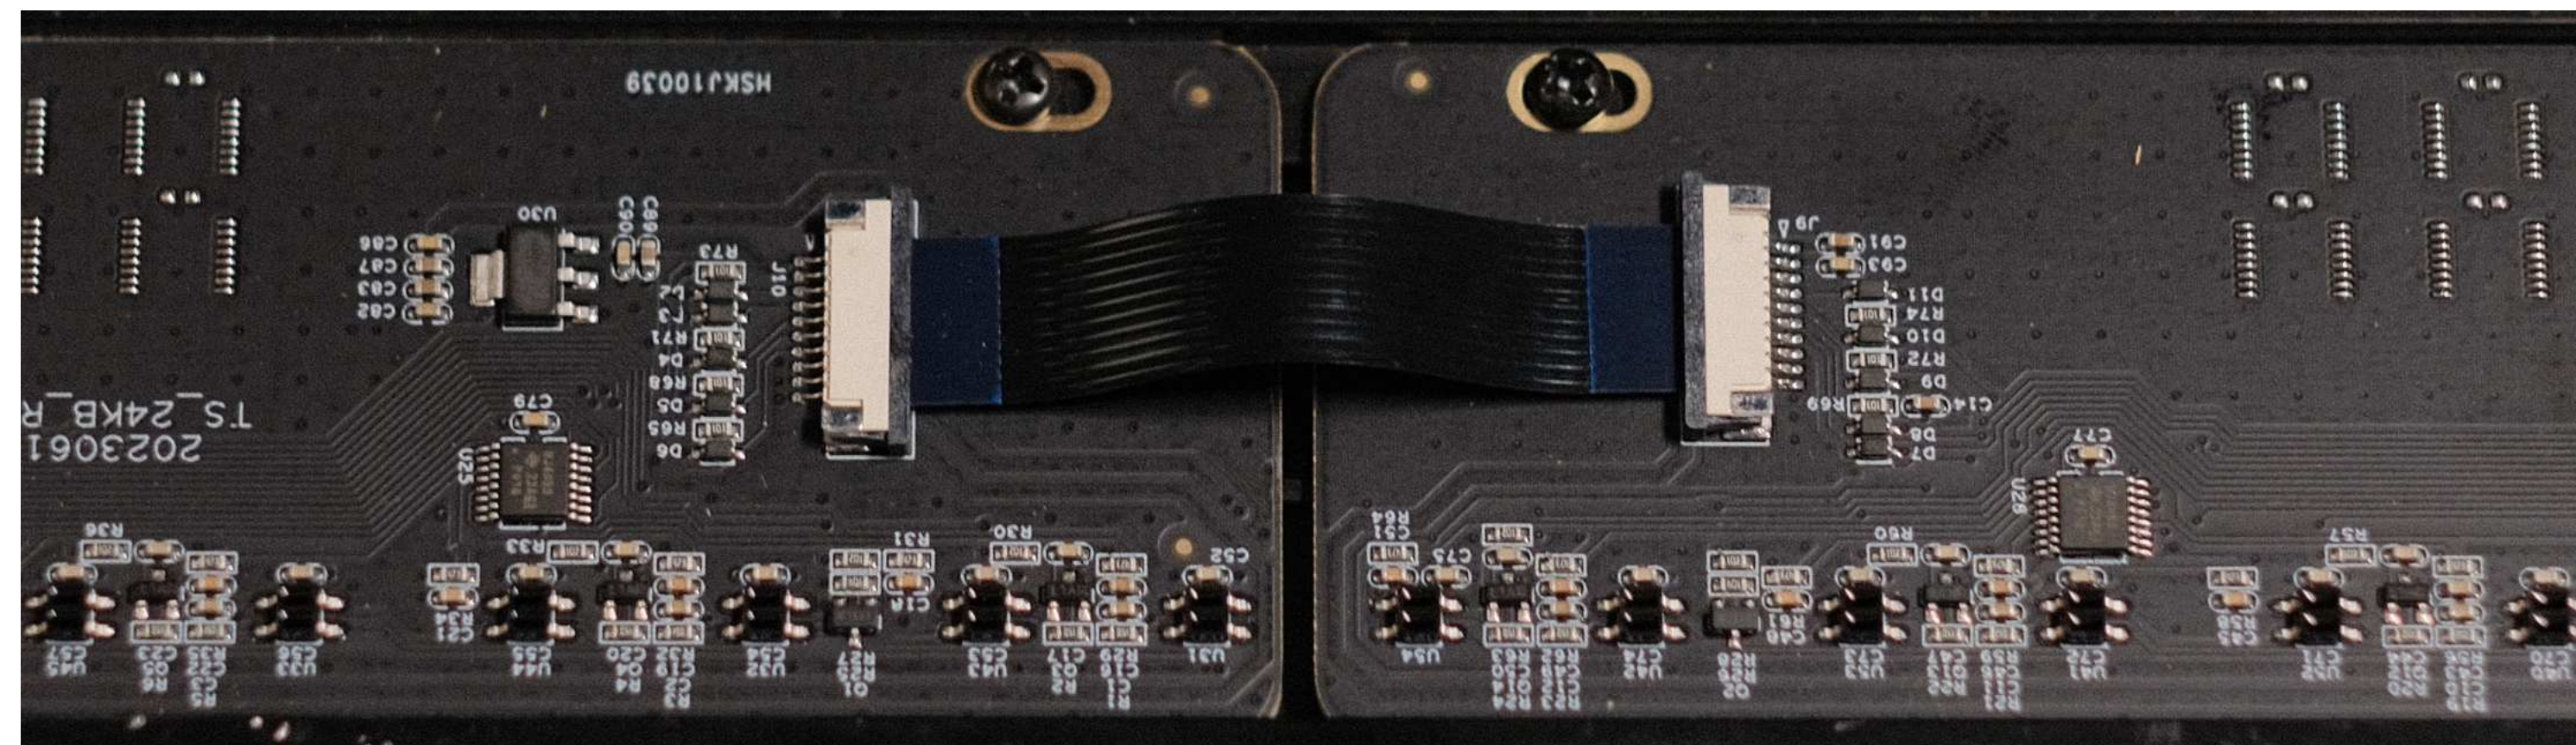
Zwei Kreuzschlitzschrauben oben und das Flexkabel in der Mitte.
